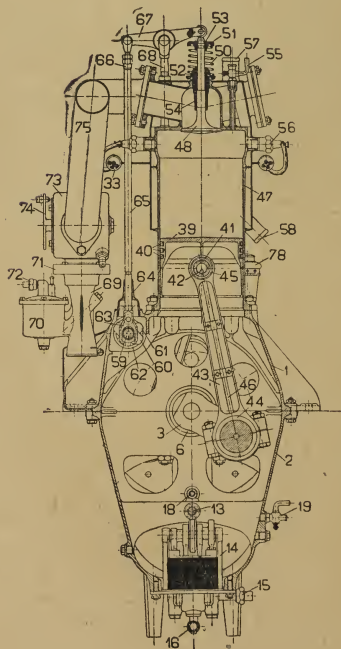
Sechszylinder-Argus-Flugmotor. Magnetseite.
